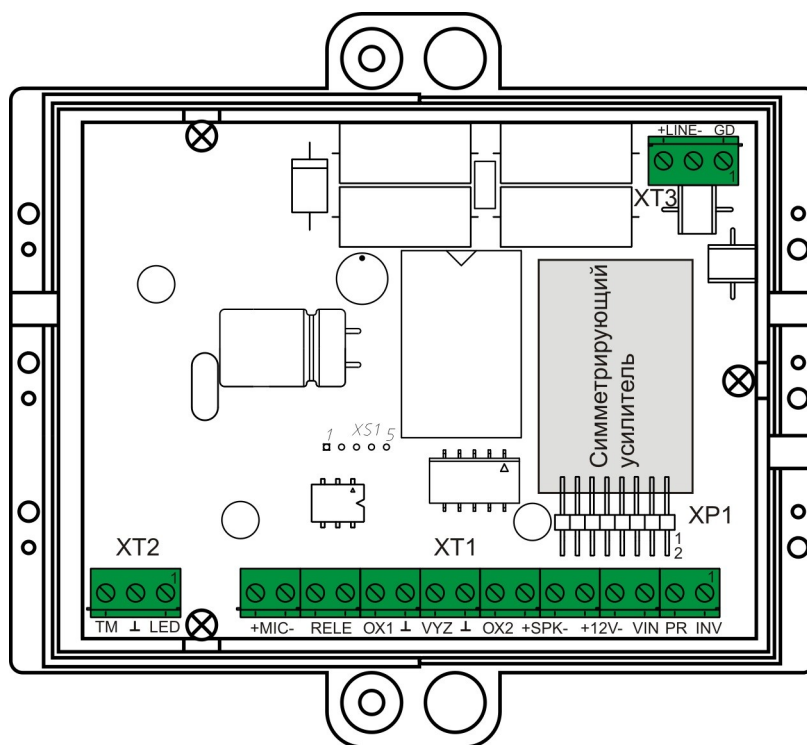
Вид на плату БЭС с клеммными соединителями
